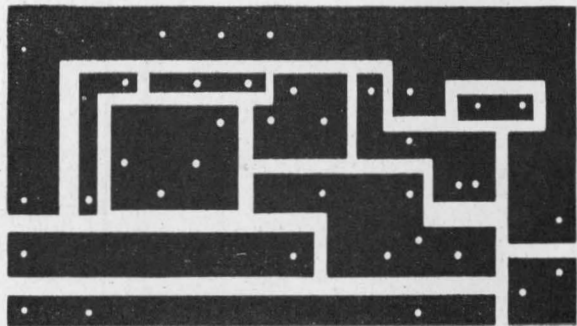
Face cobreada da plaqueta de circuito impresso confeccionada pelo Autor.
